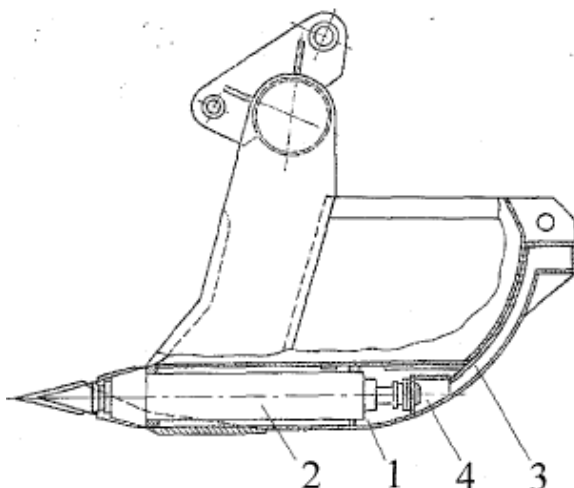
Конструкция ковша экскаватора по а.с. № 207809: 1 - полость; 2 - пневмоударный механизм; 2 - канал для подвода сжатого воздуха; 4 - распределительная коробка
